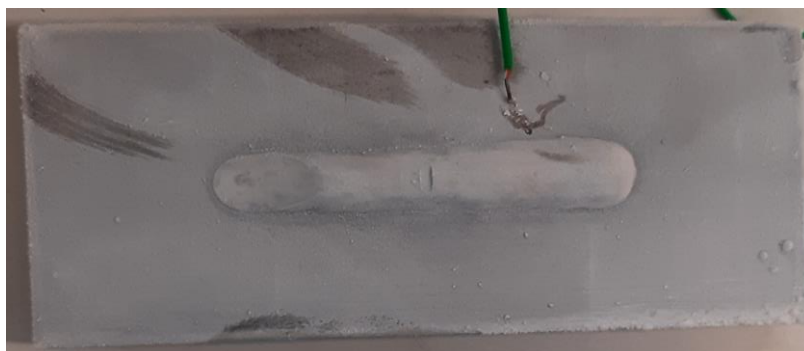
Entalhe no cordão de solda do corpo de prova após ensaio DWT.
